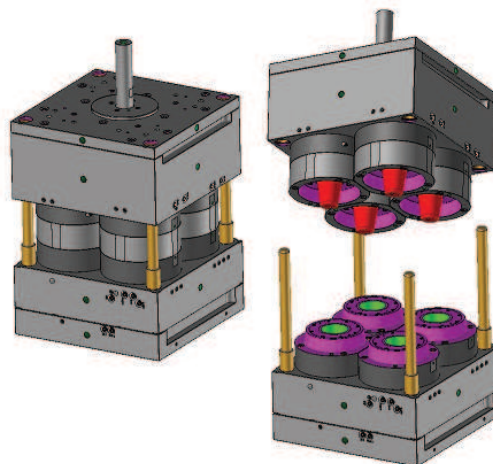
Molde de duas placas-Molde solido (MS).
